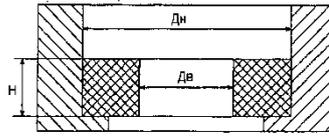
Обмежувальна оправка для зміни розмірів циліндричної Заготовки з PTFE з TRPAGG OD
